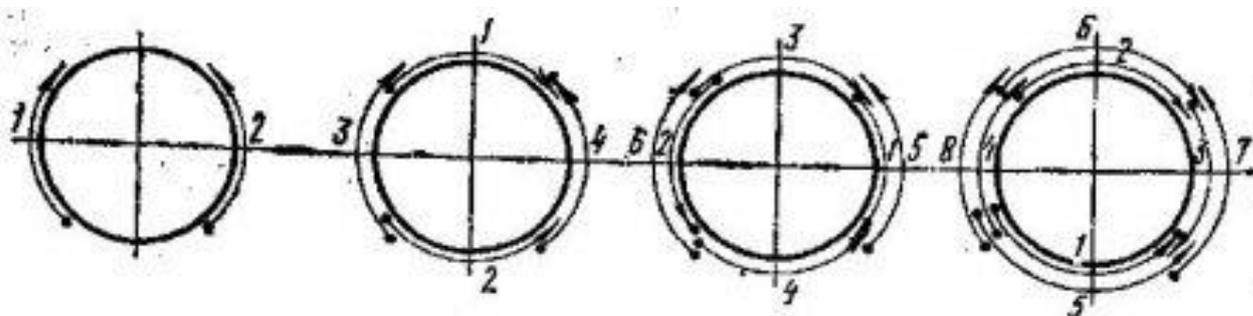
Схема сварки стыка трубы по второму методу
